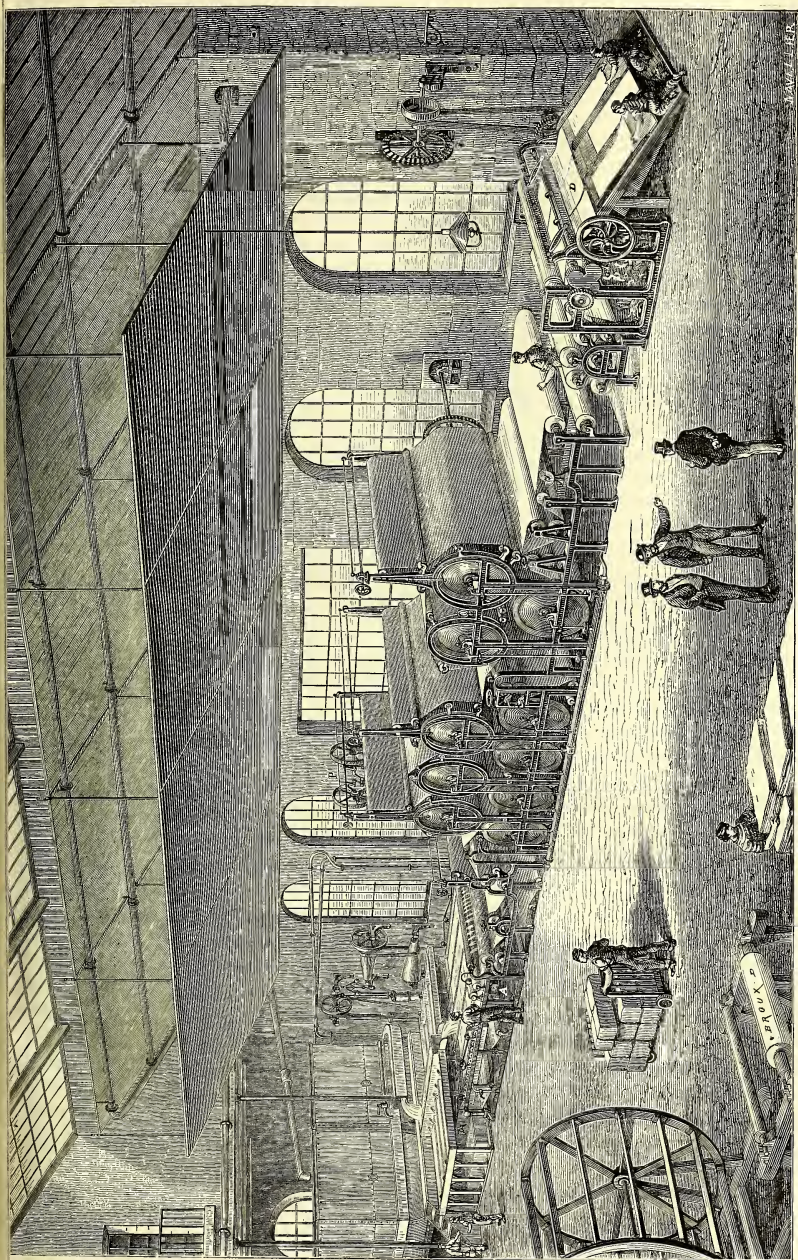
Grande machine pour la fabrication du papier continu (type Bertram).
